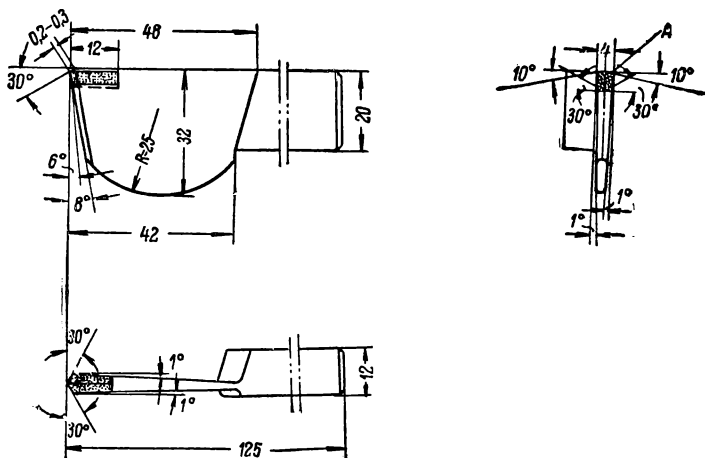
Отрезной резец конструкции Н. Г. Кузовкина.
